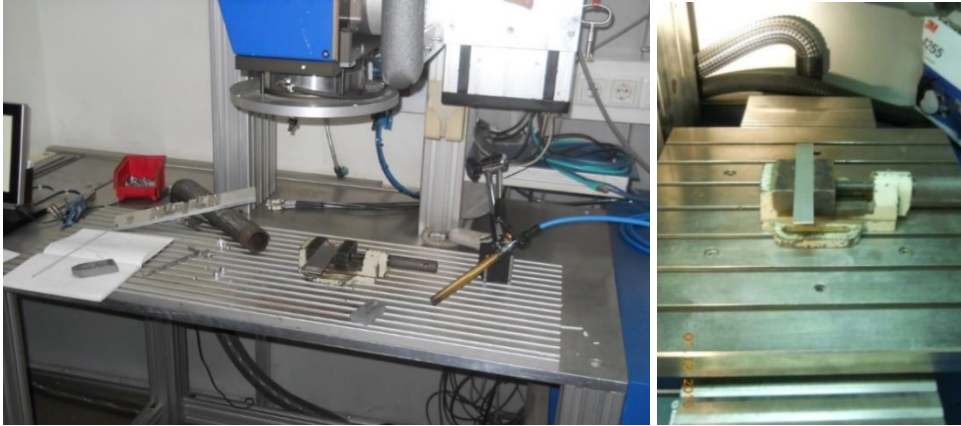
RUB LASER laboratuvarındaki kaynak makinası kamerasının görüntüsü
